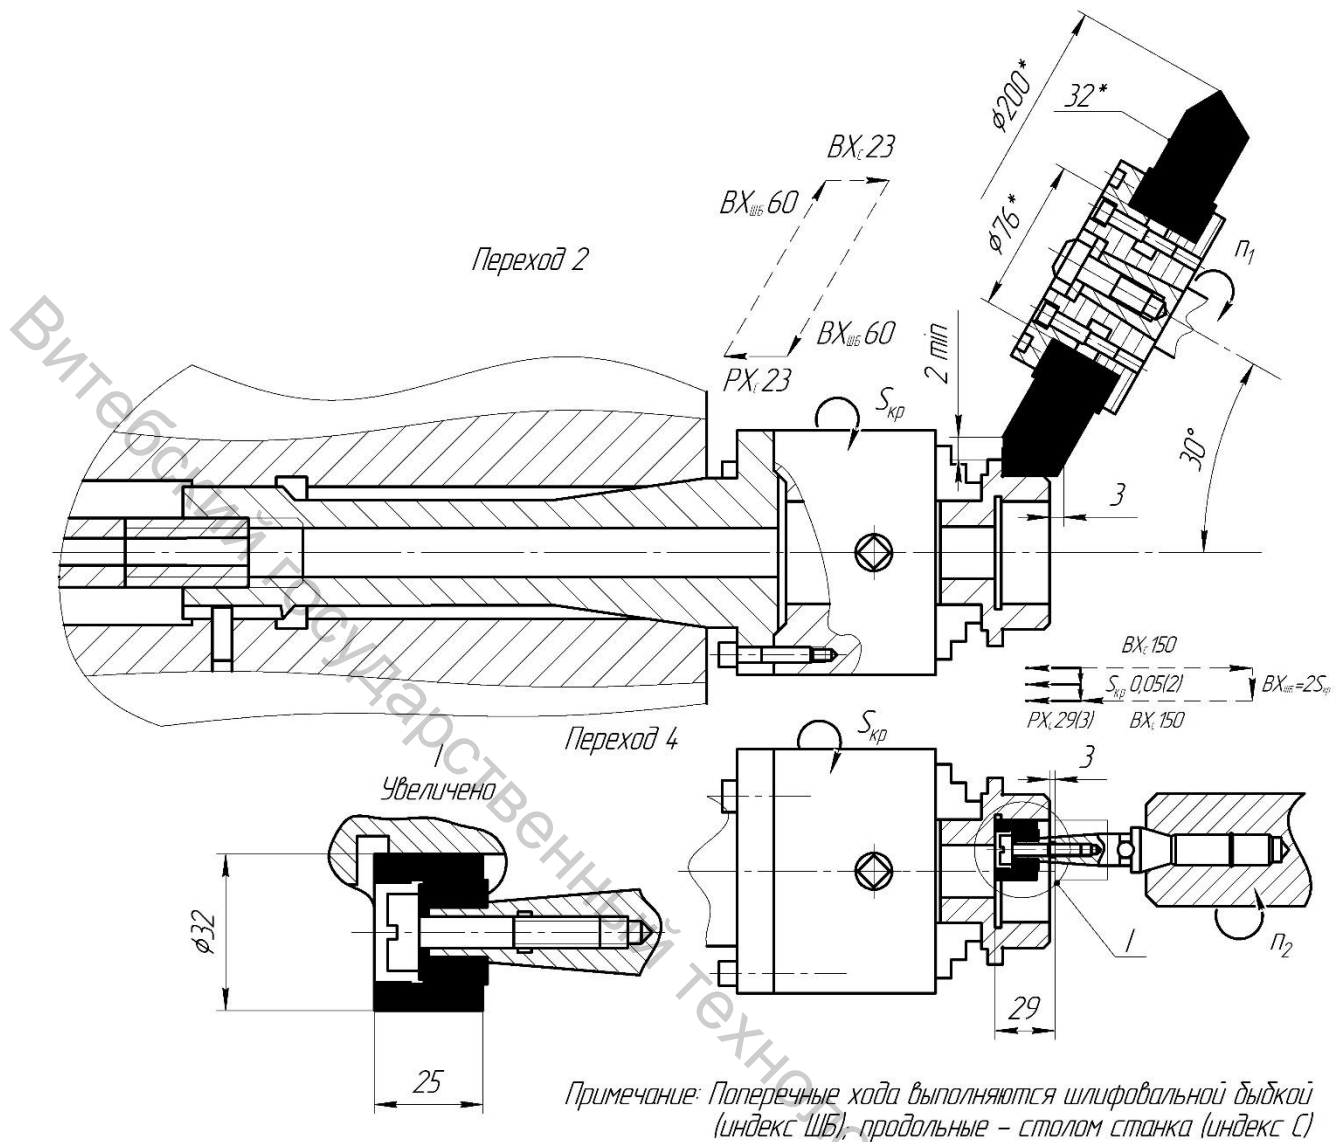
Схемы наладок универсального круглошлифовального станка 3В110 на операцию обработки детали «Втулка»
